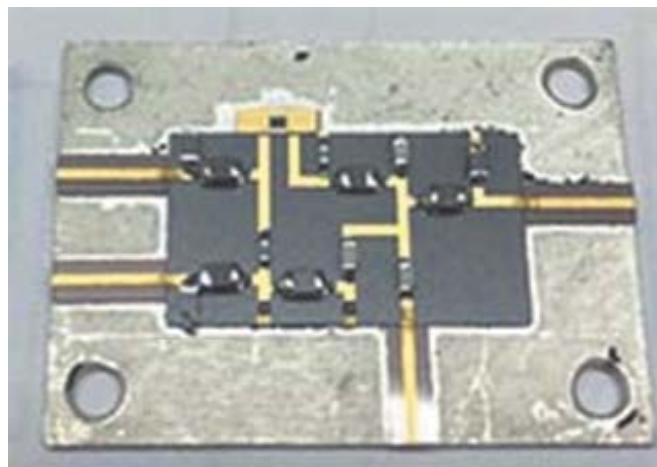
Внешний вид изготовленного макетного образца ГУН
